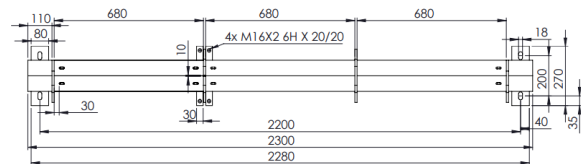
Tampak Samping *Frame Roller Conveyor
